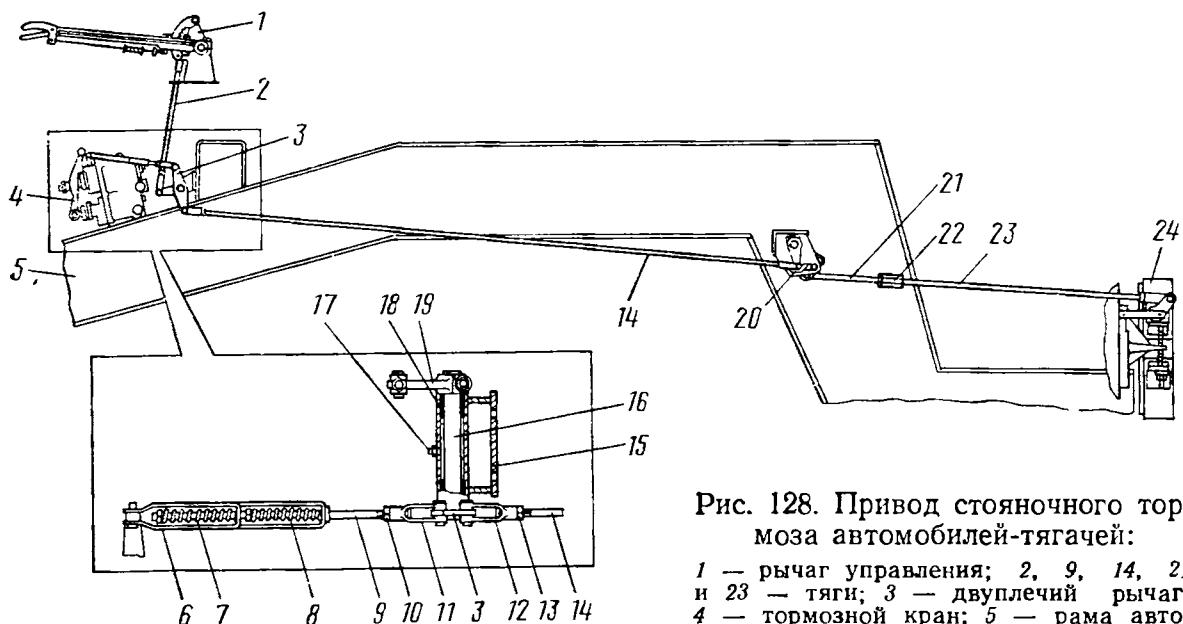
Привод стояночного тормоза автомобилей-тягачей:
